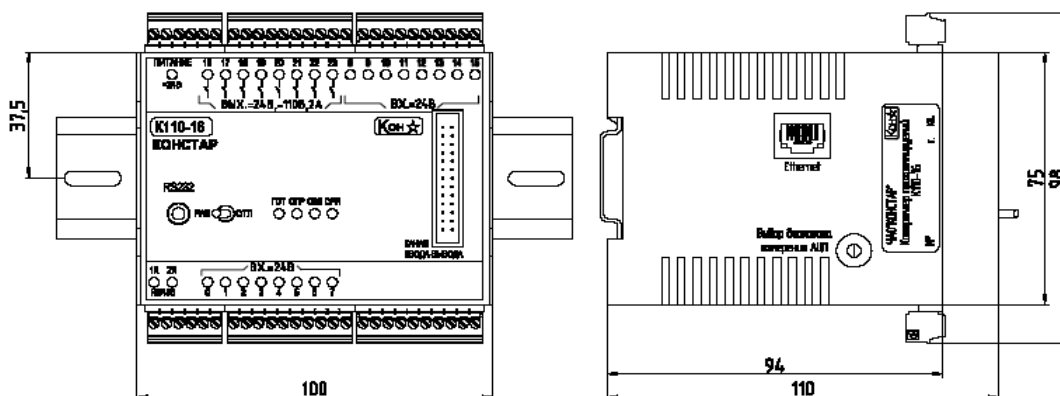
Габаритные и установочные размеры базового блока K110
